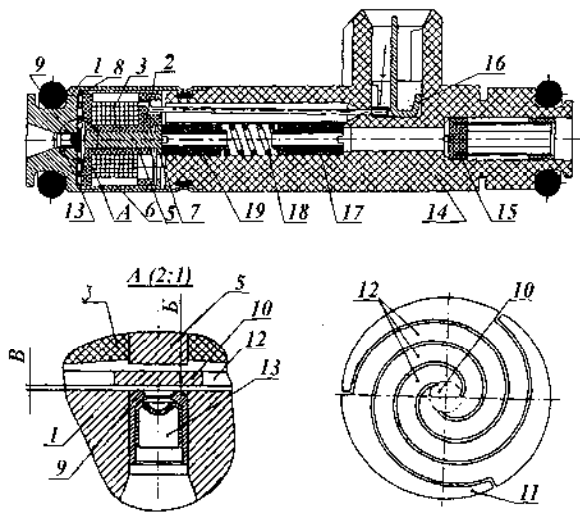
Конструкция экспериментальной форсунки инжекторного ДВС: 1 - корпус из немагнитного материала; 2 - электромагнит; 3 - катушка электромагнита; 4 - цельный магнитопровод; 5 - сердечник; 6 - корпус; 7 - основание; 8 - запорный элемент из магнитного материала; 9 - опорное седло; 10 - центральная часть запорного элемента; 11 - периферийная часть запорного элемента; 12 - упругие элементы; 13 - распылитель; 14 - коллектор подключения к топливной системе; 15 - фильтр; 16 - клеммы подключения электромагнита; 17 - винт; 18 - винтовая пружина; 19 - упор
